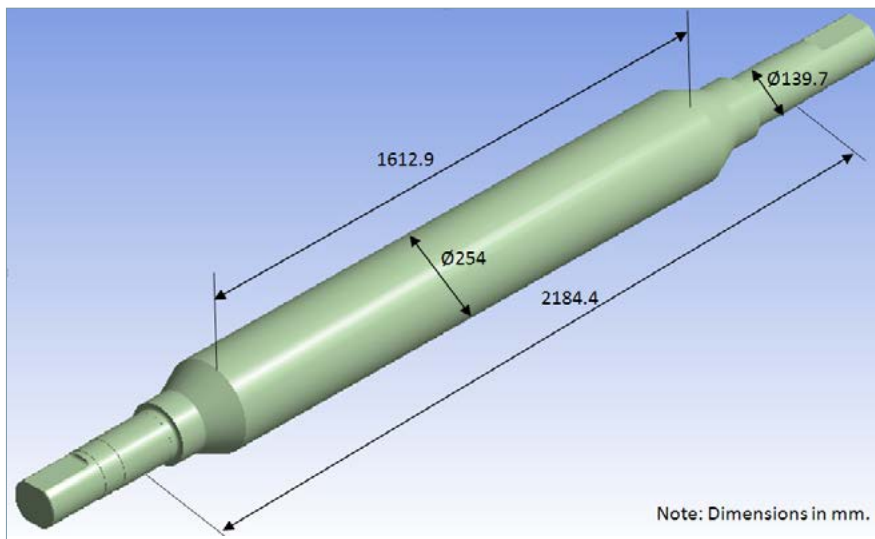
Diseño de rodillo de trabajo; vista isométrica
